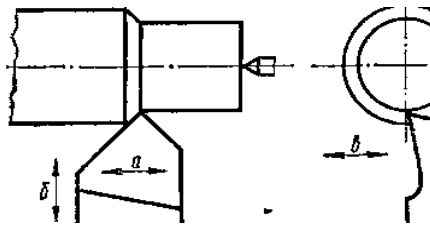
Коливальні рухи інструмента в процесі обробки
